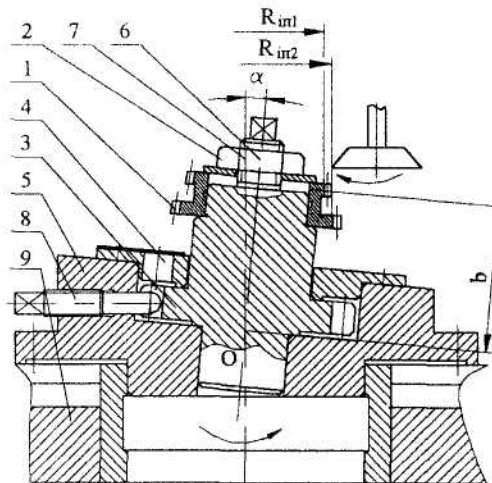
Схема пристрою для обробки зубів сателіта для зубодовбального верстата:
